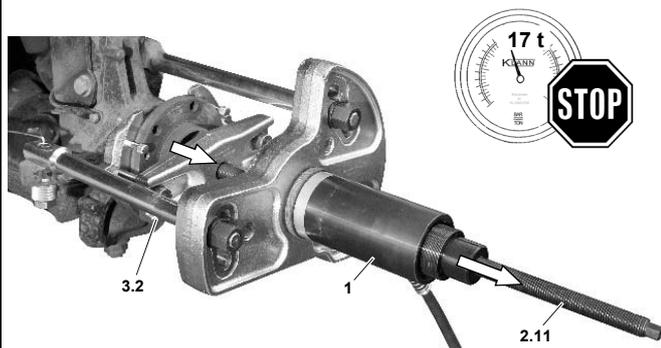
Enlever l'unité moyeu/roulement de roue et l'ensemble plaque de traction/pression.
